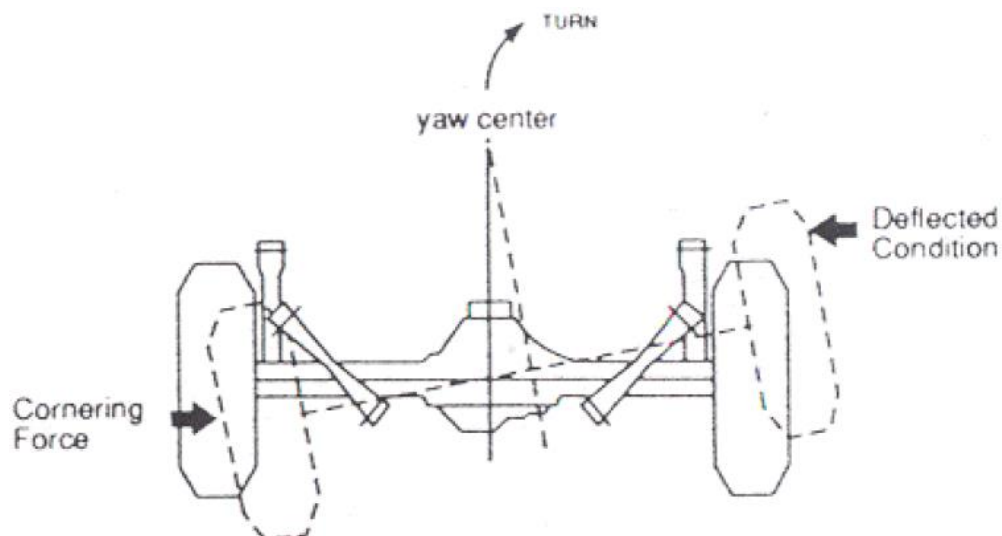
Přední a zadní nápravnice - OPEL Omega [20]
